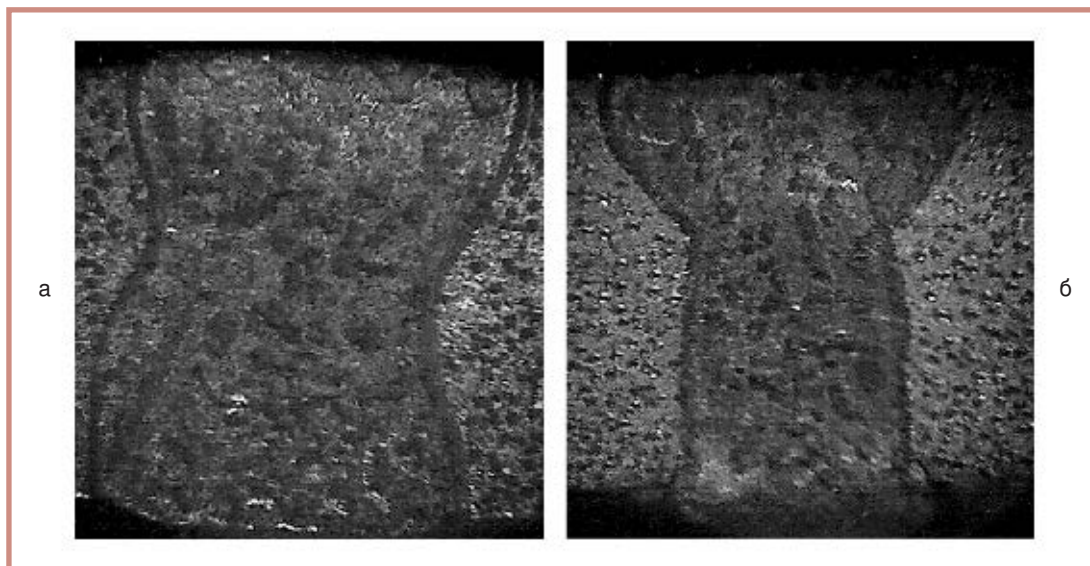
Изменение формы шва при сварке стыковых соединений из стали 10X18H10T ($\delta=1,5$ мм) непрерывным излучением волоконного лазера мощностью 400 Вт: а — защита Ar с расходом 14 л/мин, скорость сварки 30 м/ч, заглупление фокуса 0,3 мм; б — давление $1,5 \cdot 10^{-2}$ торр, скорость сварки 30 м/ч, заглупление фокуса 0,3 мм
